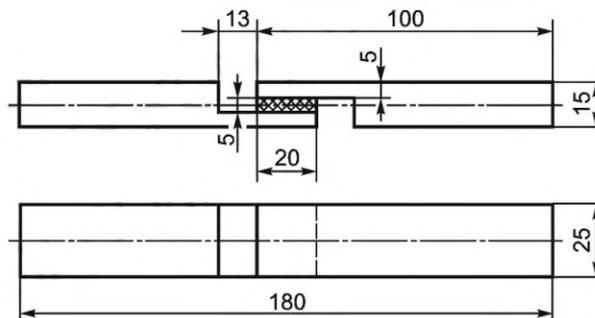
Пример образца для испытаний на прочность соединений низкопрочными клеями
